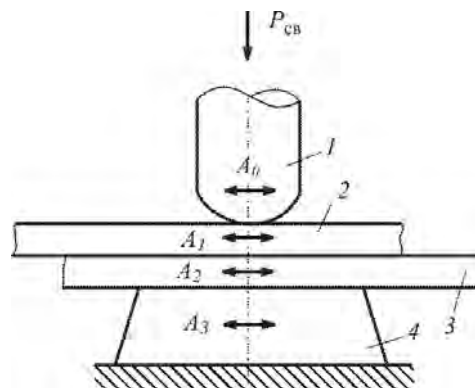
Схема ультразвуковой сварки металлов:
